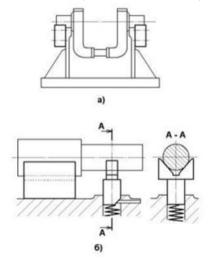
Примеры установки заготовок наружной цилиндрической поверхностью: а) коленчатого вала на 2 призмы; б) –ступенчатого вала в призмы с использованием самоустанавливающейся опоры.
